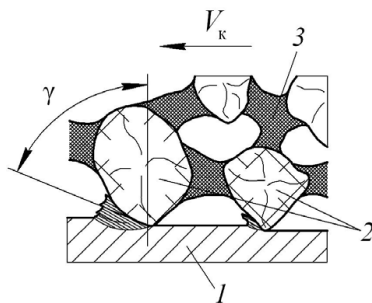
Схема резания абразивным инструментом: 1 – шлифуемый металл; 2 – абразивное зерно; 3 – связка
